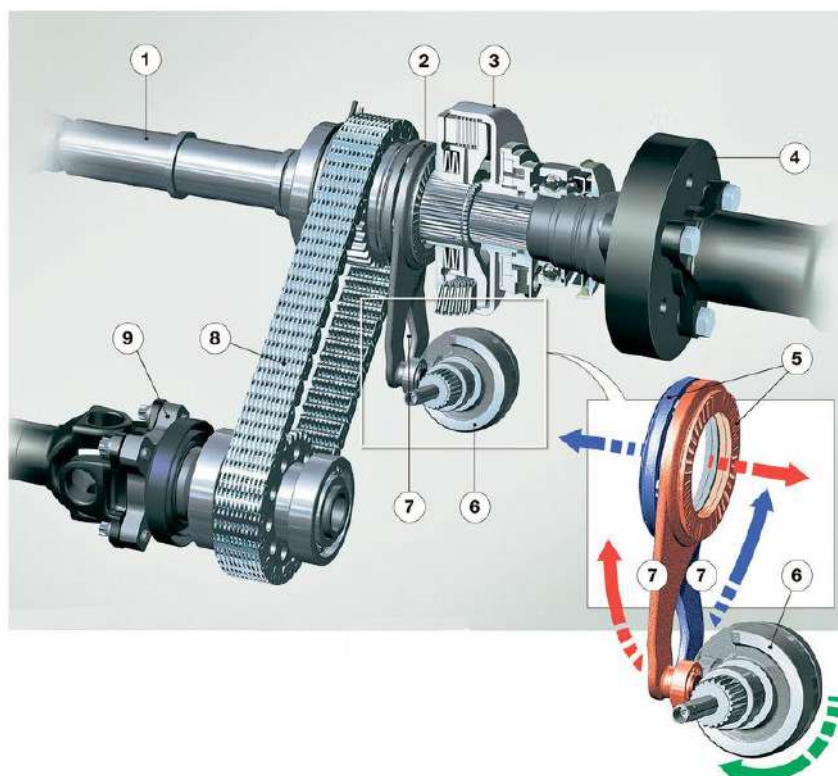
Конструкция раздаточной коробки xDrive с цепным приводом
